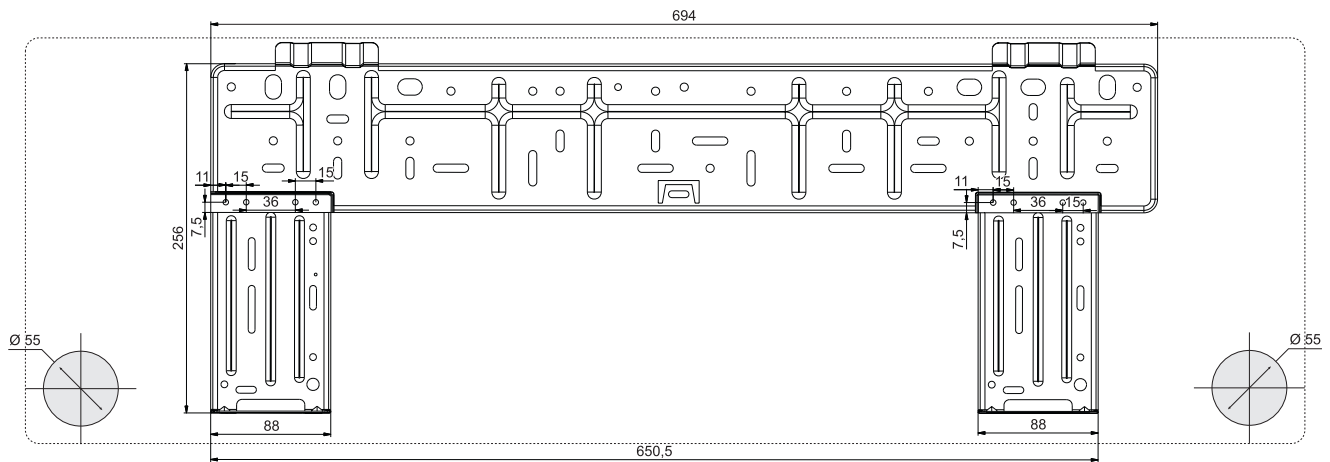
Placa de montaje para VAI 6-050 WMNI.
